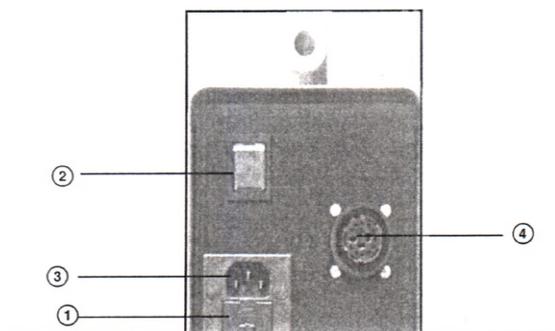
Vista da face traseira da unidade de controle ID Weld 2500
